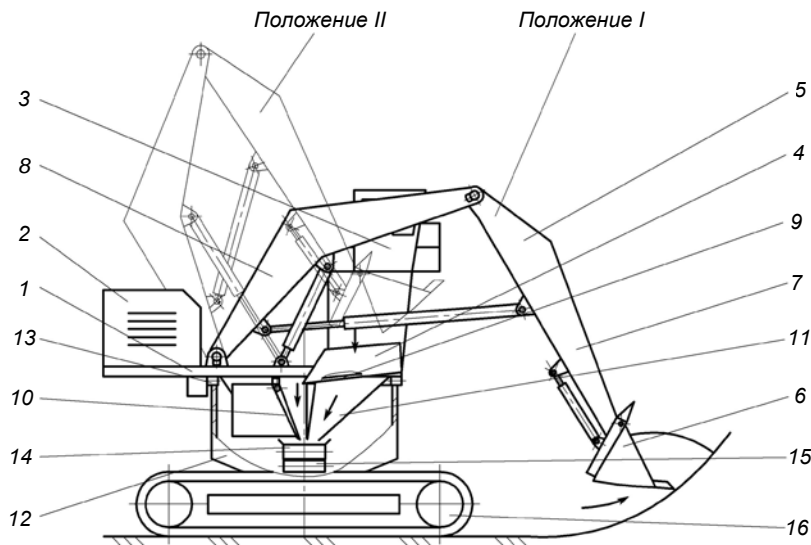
Конструкция выемочно-дробильного агрегата.
